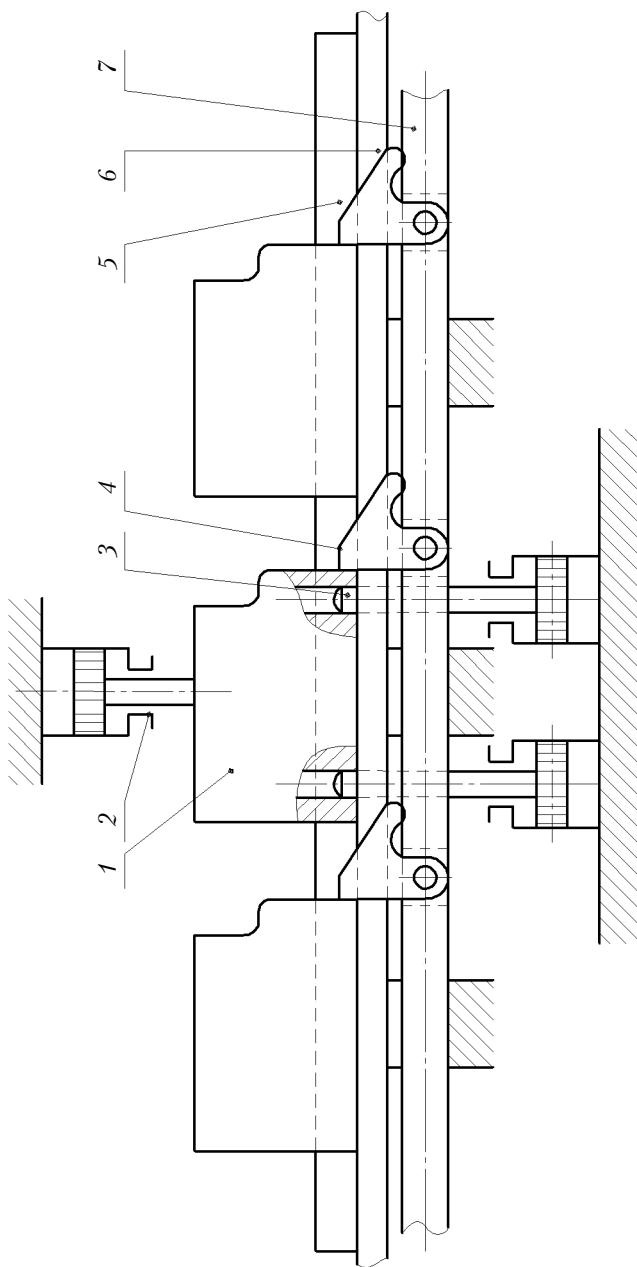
Схема приспособления для перемещения заготовки или приспособления спутника
